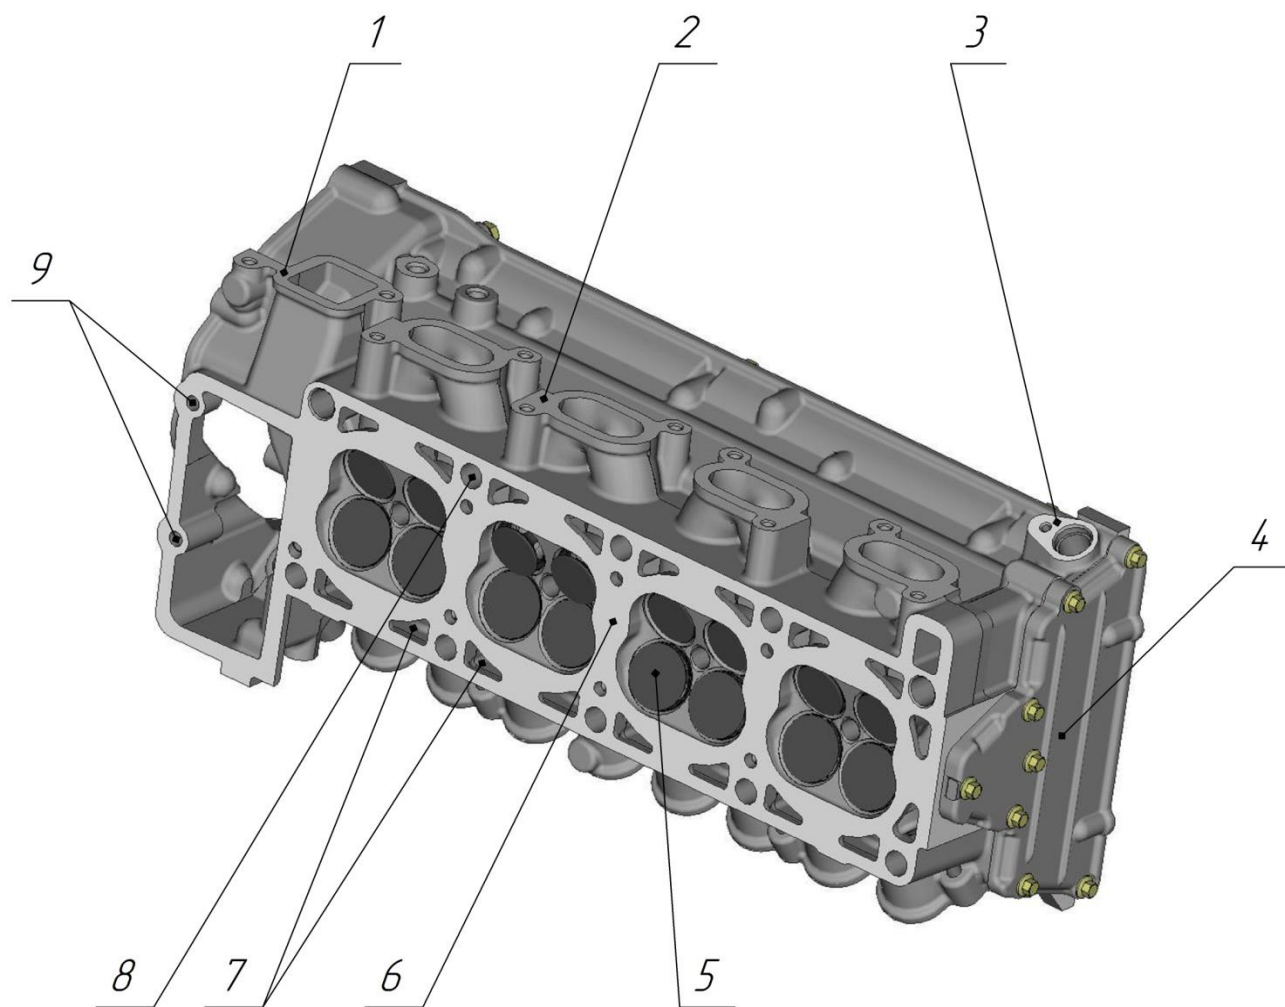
Головка цилиндров. Вид на камеры сгорания, на фланец выпускного коллектора и на заднюю крышку:
